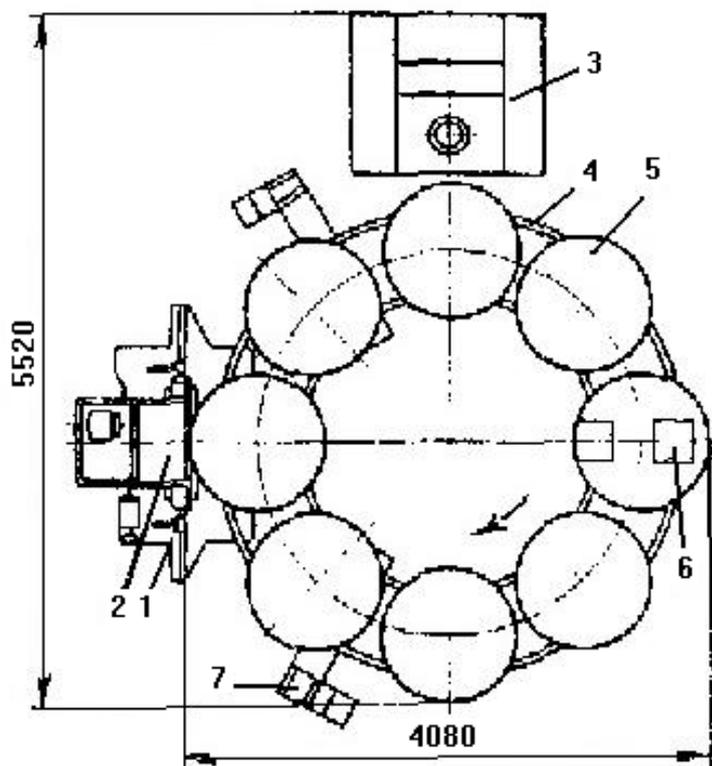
Тестоприготовительный агрегат Ш2-ХБВ:
